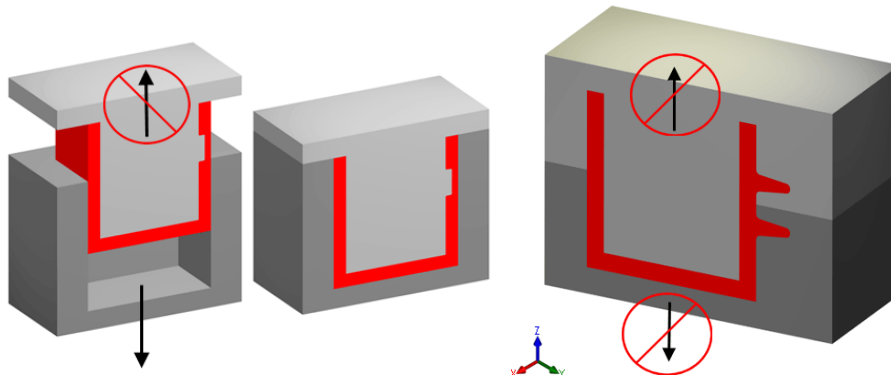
Bajo relieve interno (izquierda) y bajo relieve externo (derecha) [19]
